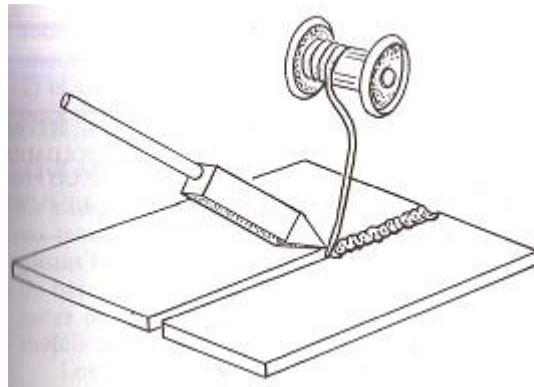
Proceso de la soldadura con bajo punto de fusión.
